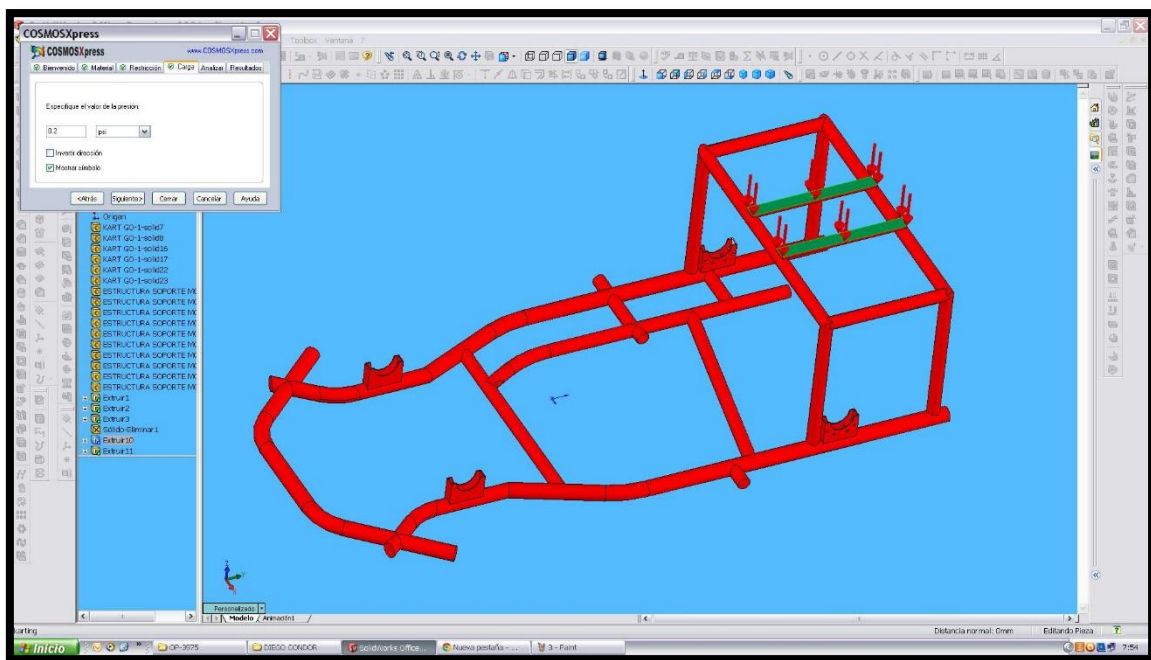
Carga Aplicada sobre el soporte del motor SolidWorks
